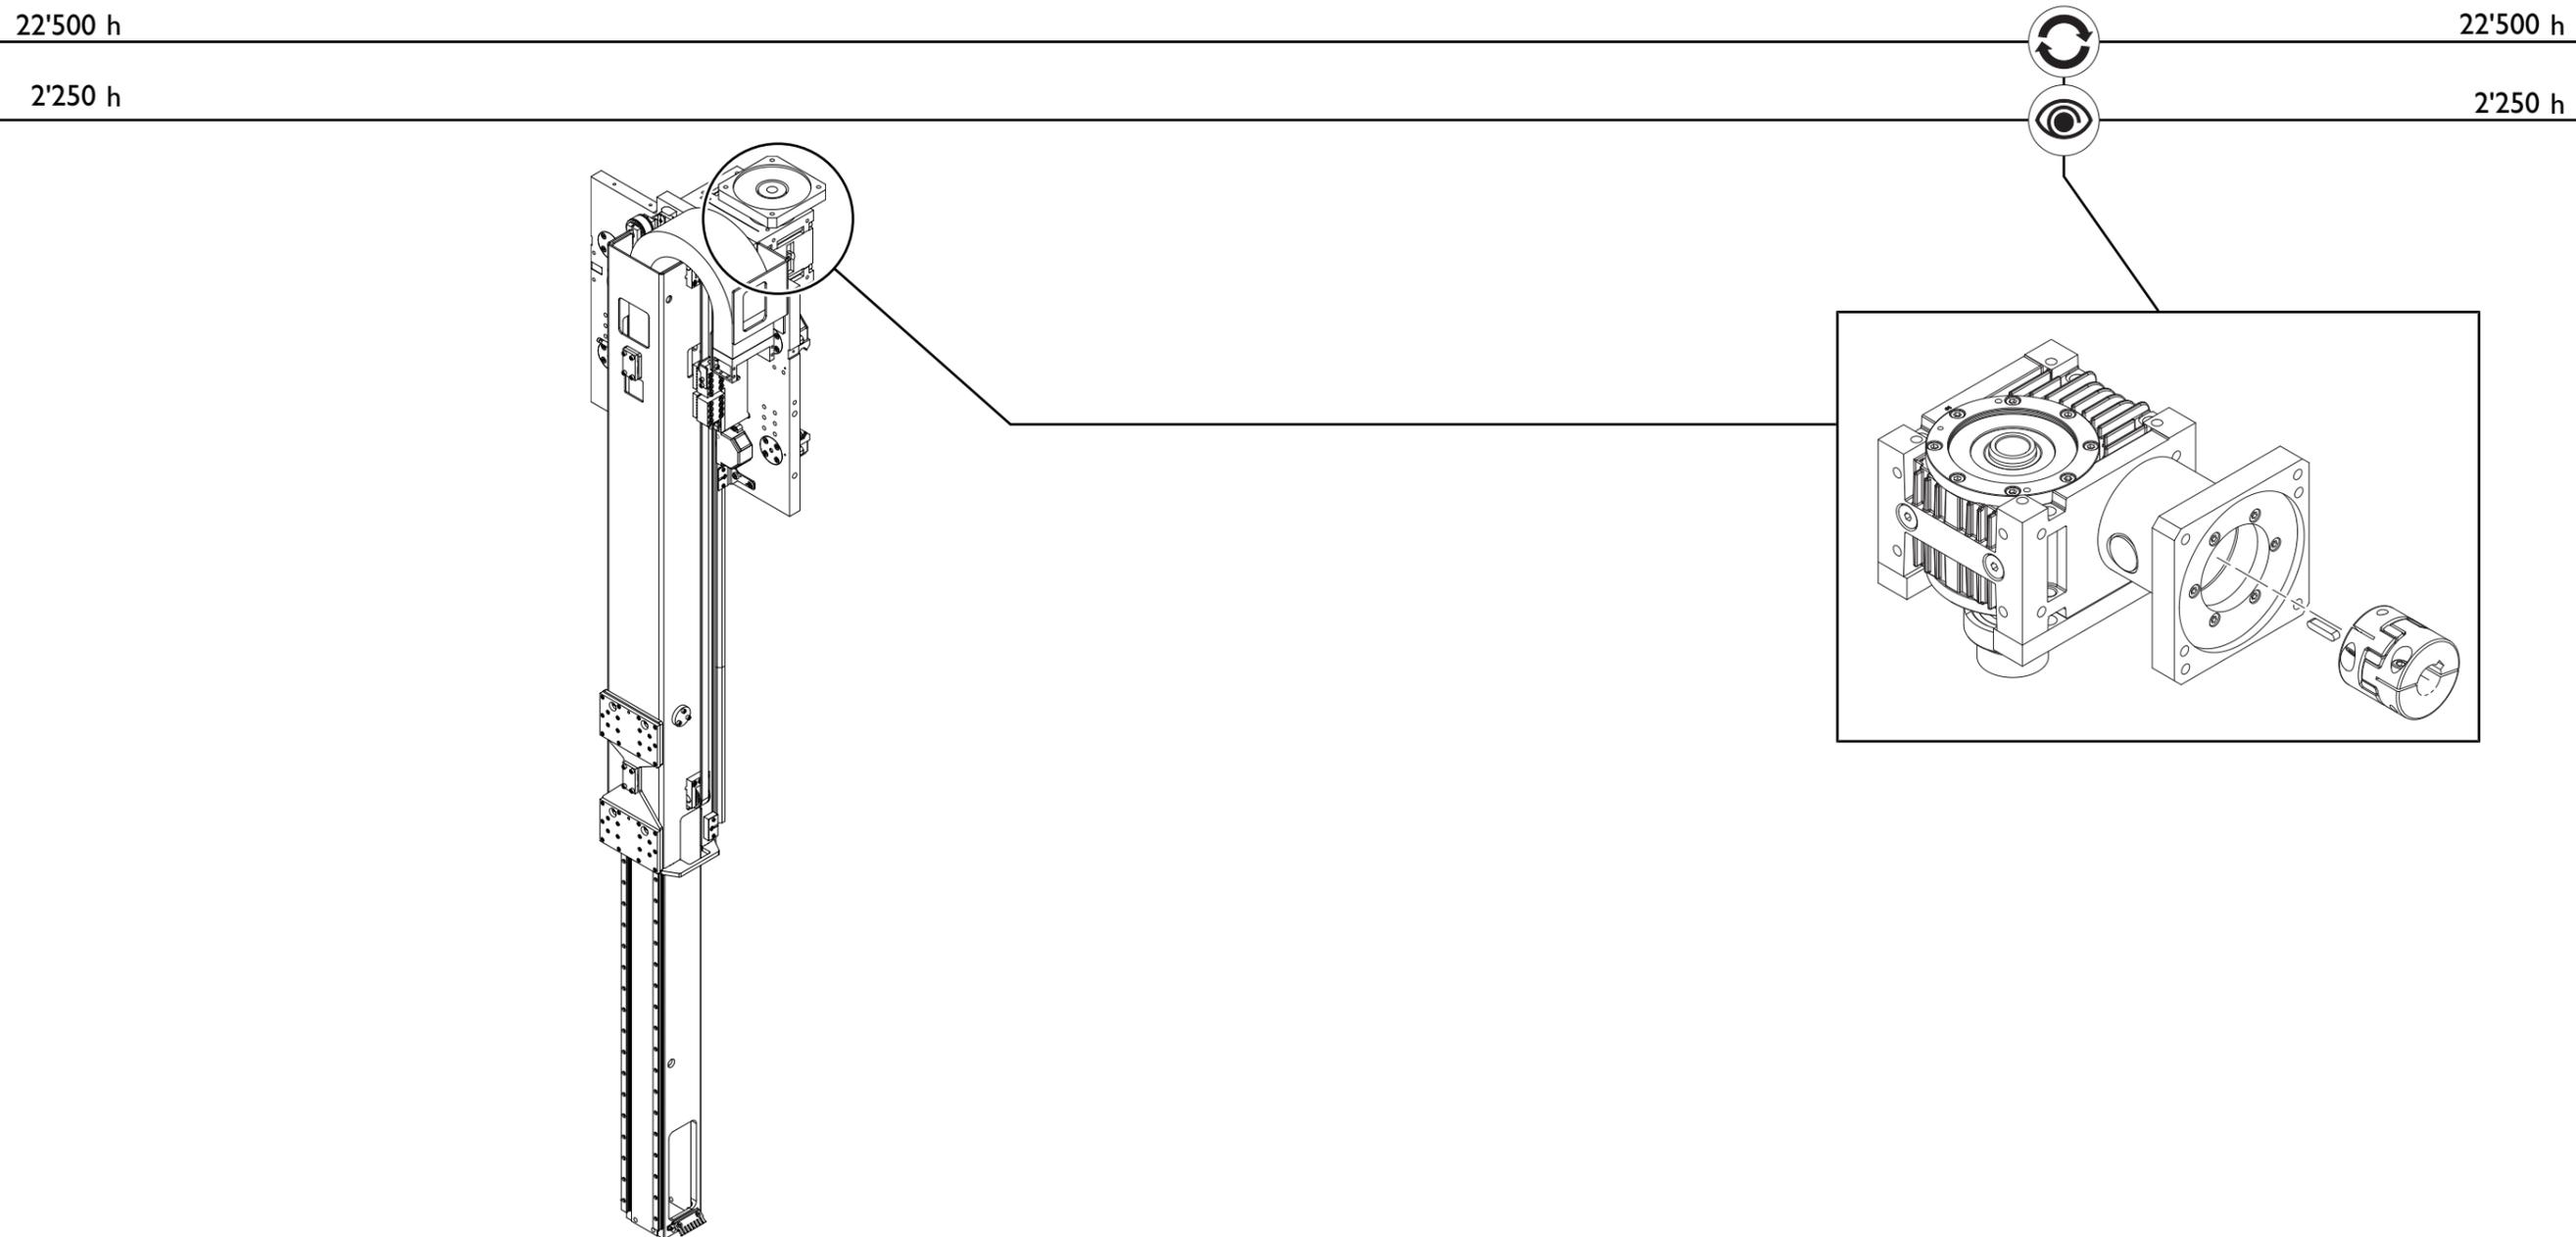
План техобслуживания: Блок редуктора Güdel
